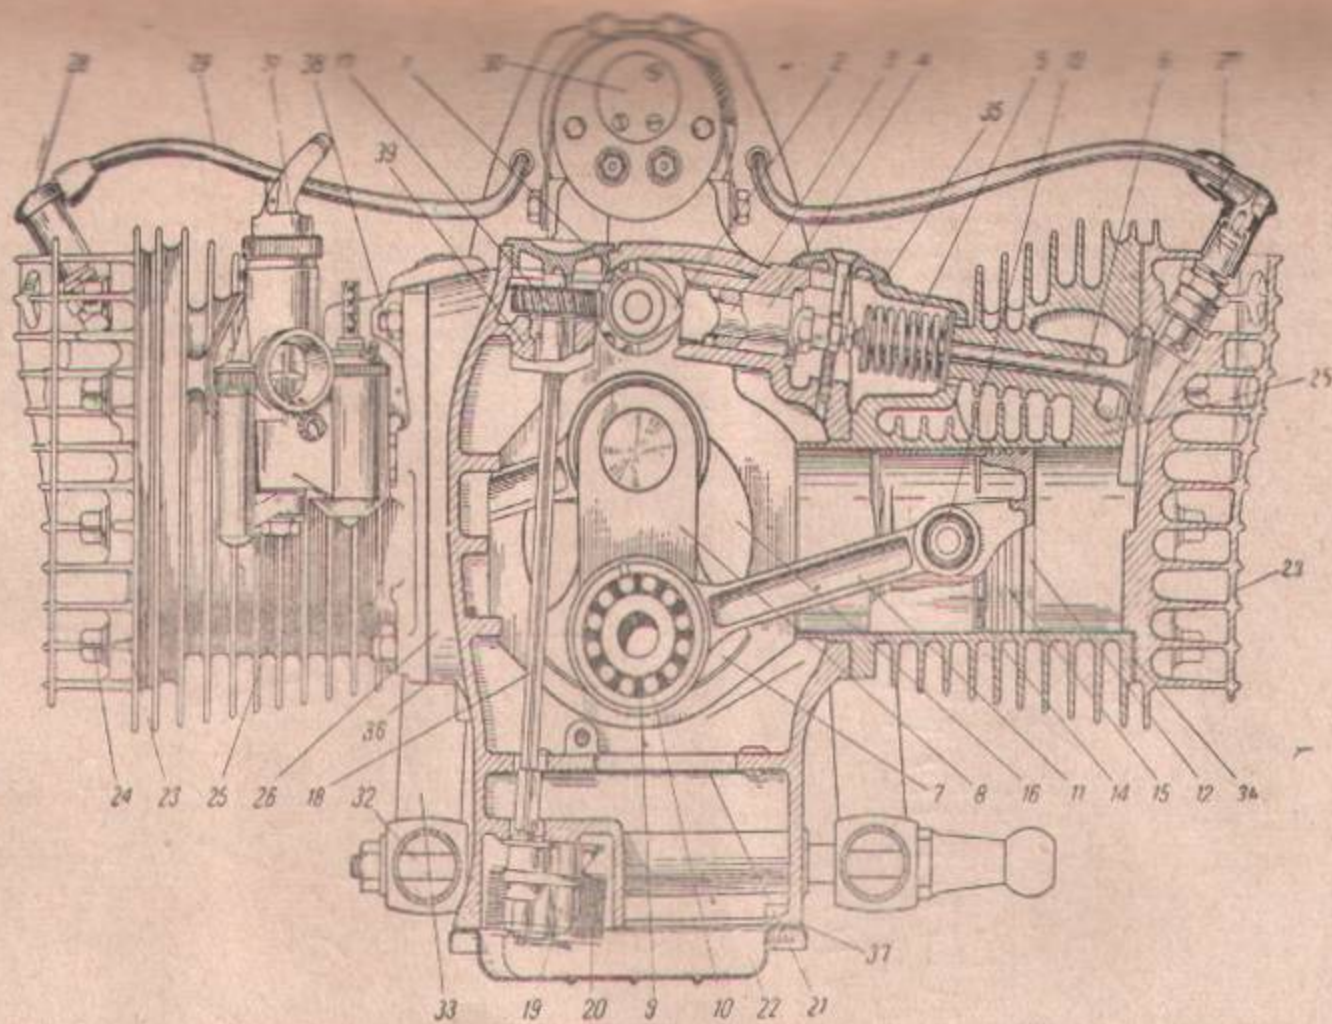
Двигатель мотоцикла М-72 (поперечный разрез);
